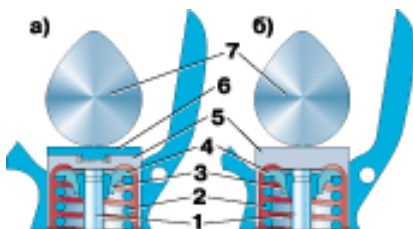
Узел регулировки зазоров в приводе клапанов двигателя F3R 272: а – конструкция регулировочного узла двигателей до № 13559; б – конструкция регулировочного узла двигателей с № 13559; 1 – клапан; 2 – пружина клапана; 3 – сухарь; 4 – тарелка пружины; 5 – толкатель; 6 – регулировочная шайба; 7 – кулачок распределительного вала
